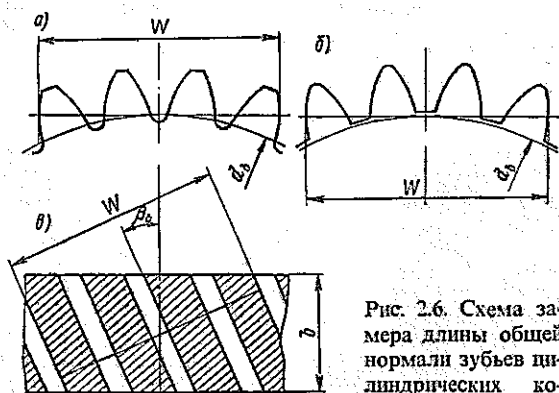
Схема замера длины общей нормали зубьев цилиндрических колес:
